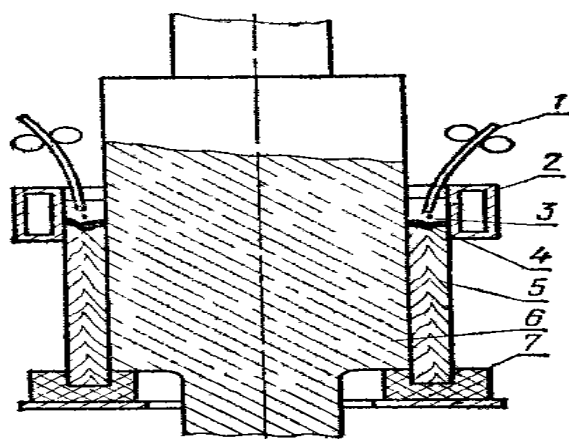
Схема електрошлакового наплавлення циліндричної поверхні: 1 — електрод; 2 — мідний охолоджуваний повзун; 3 — ванна розплавленого шлаку; 4 — металічна ванна; 5 — наплавлений метал; 6 — деталь, що наплавається; 7 — графітова підкладка
